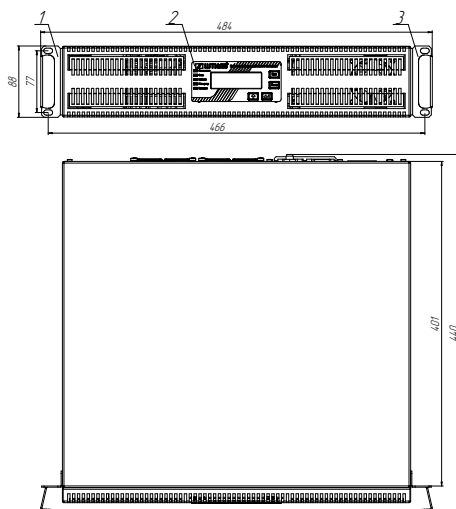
Габаритные размеры и компоненты передней панели ИБП Штиль SR1102L, SR1103L и SR1103TL
